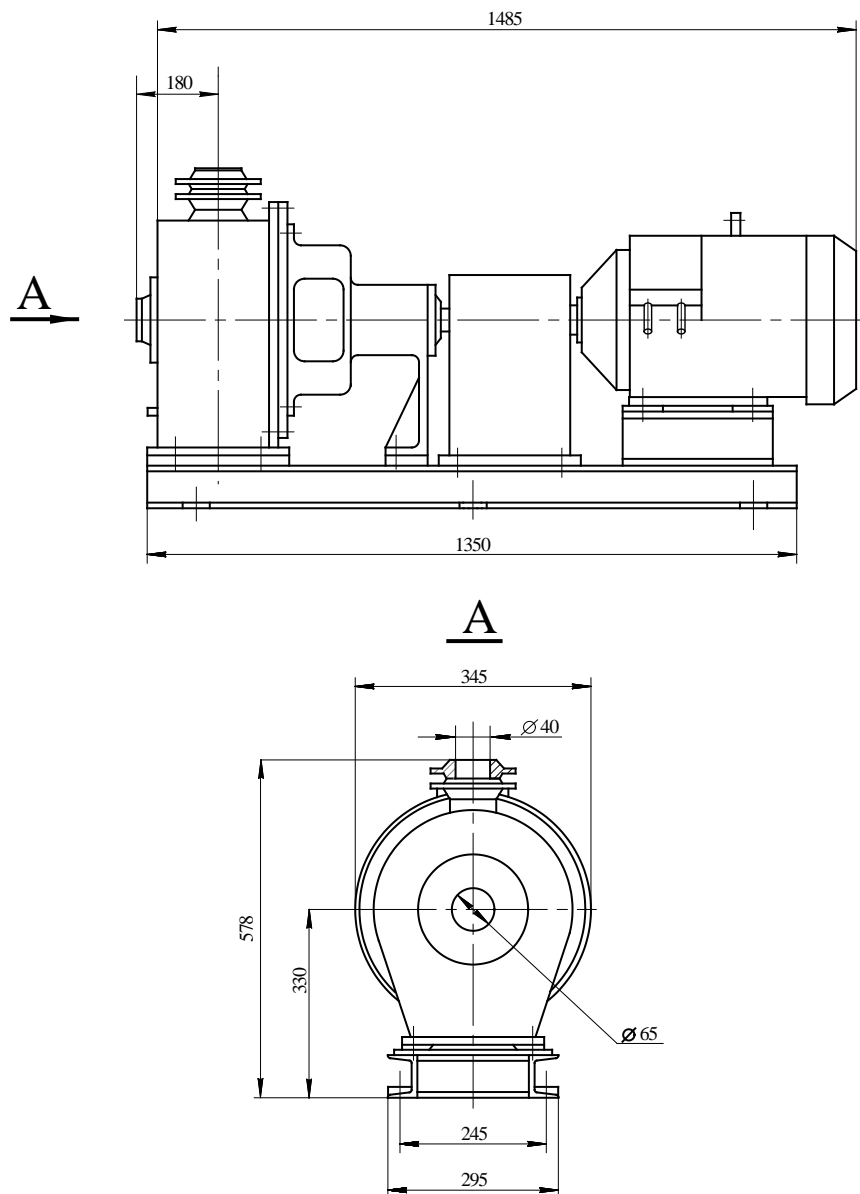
Габаритный чертеж насоса контрольных баков типа ЦНА 25/52
